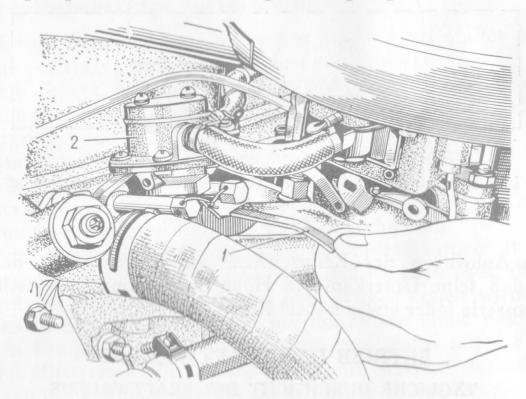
Lage der Kraftstoffpumpe an Motor: I — Handbetätigungshebel der Membranpumpe; 2 — Kraftstoffpumpe
